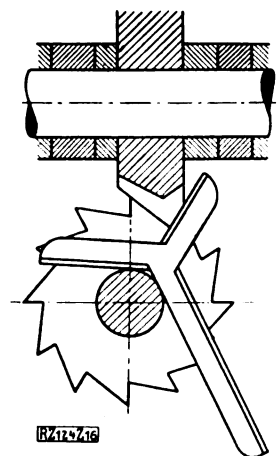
Einstellehre für Schleifscheiben und Fräser.
